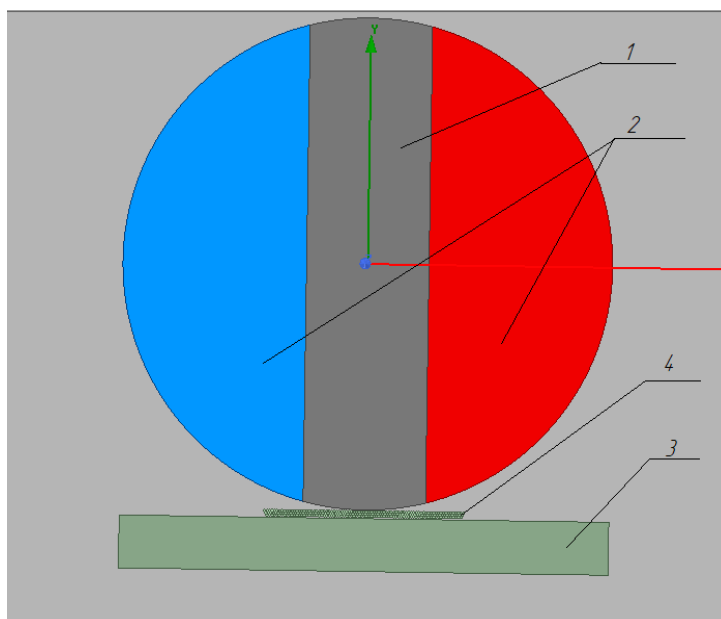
Модель для расчета магнитных сил на зерна: 1) магнит; 2) магнитопровод; 3) заготовка; 4) абразивный порошок.
